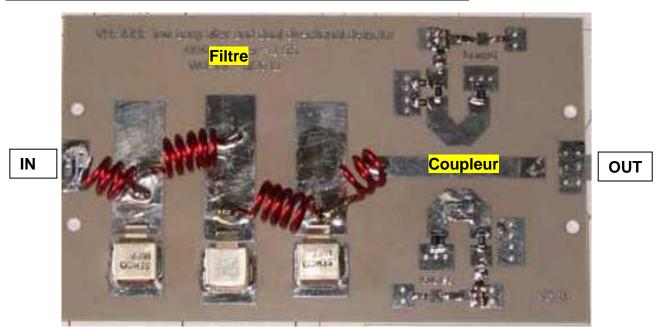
PCB du filtre passe-bas avec coupleur directionnel
